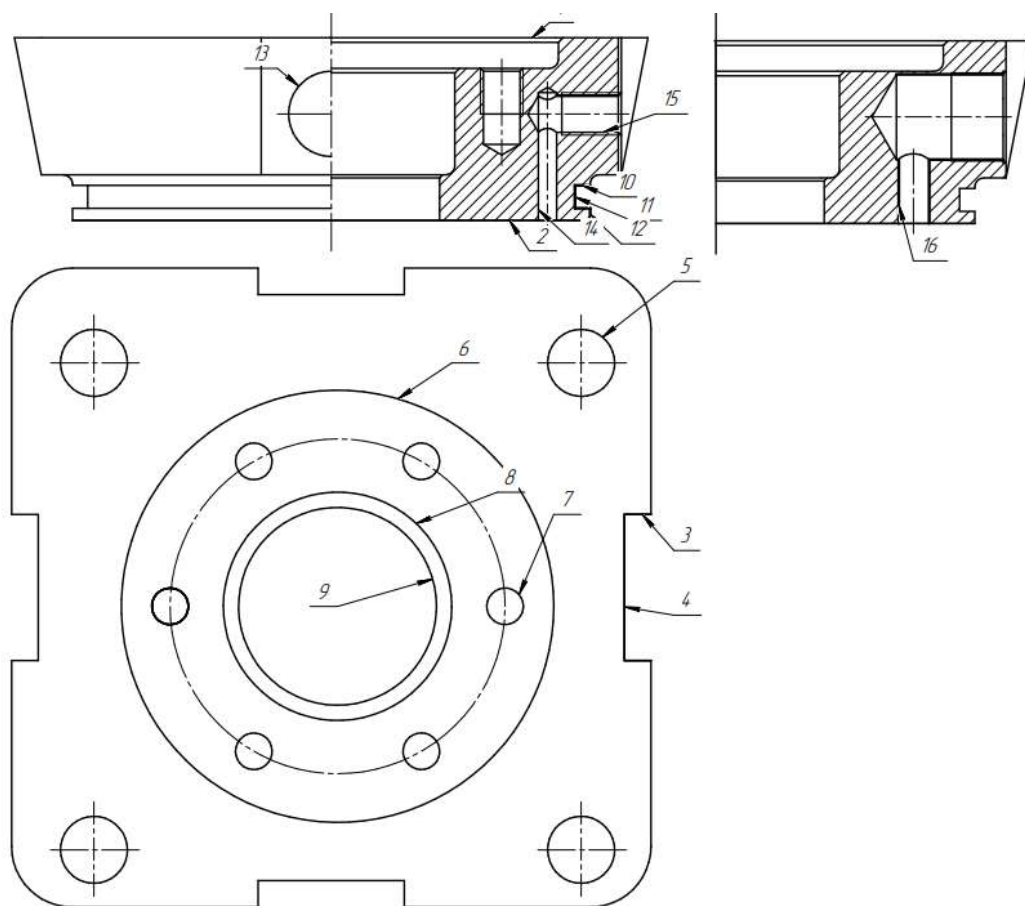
Ескіз кришки із зазначеними поверхнями під обробку
